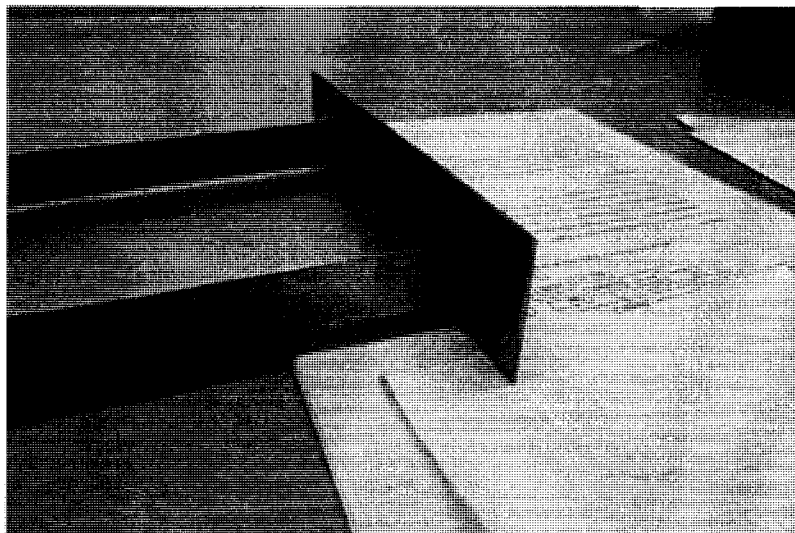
Mise à niveau du moule pour la fabrication des obstacles.
